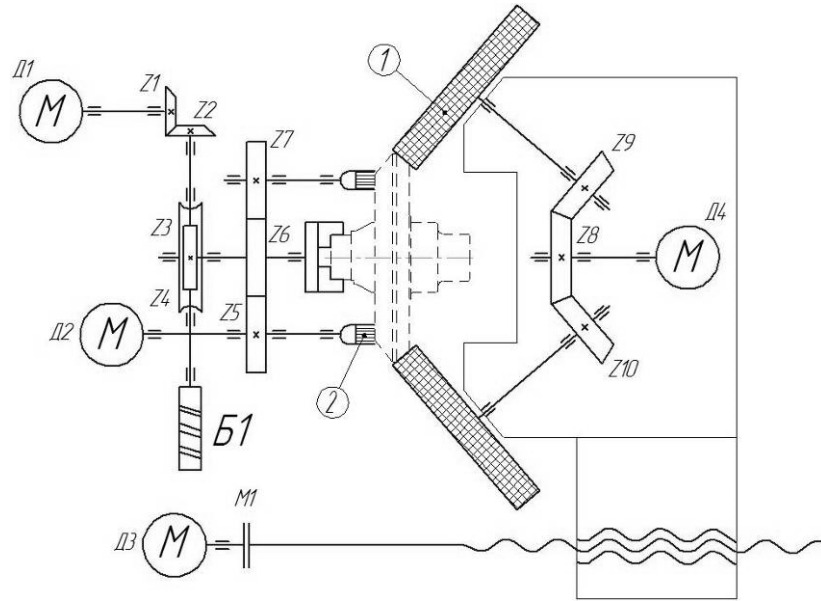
Компоновочна схема установки для зняття задирок по контуру зубчастого вінця конічної шестерні
